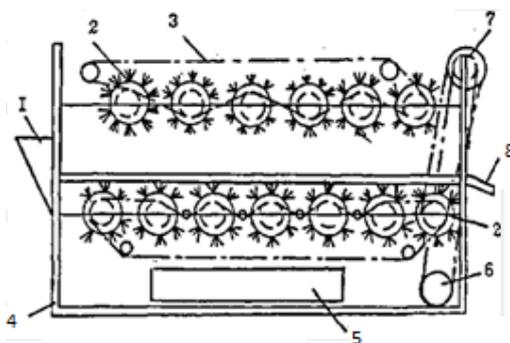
Схема щеточного очистителя корнеклубнеплодов (ЧИМЭСХ): 1 - приемный бункер; 2 - щетки; 3 - приводная цепь; 4 - рама; 5 - бункер примесей; 6 - электропривод; 7 - контрпривод; 8 - выгрузной лоток
